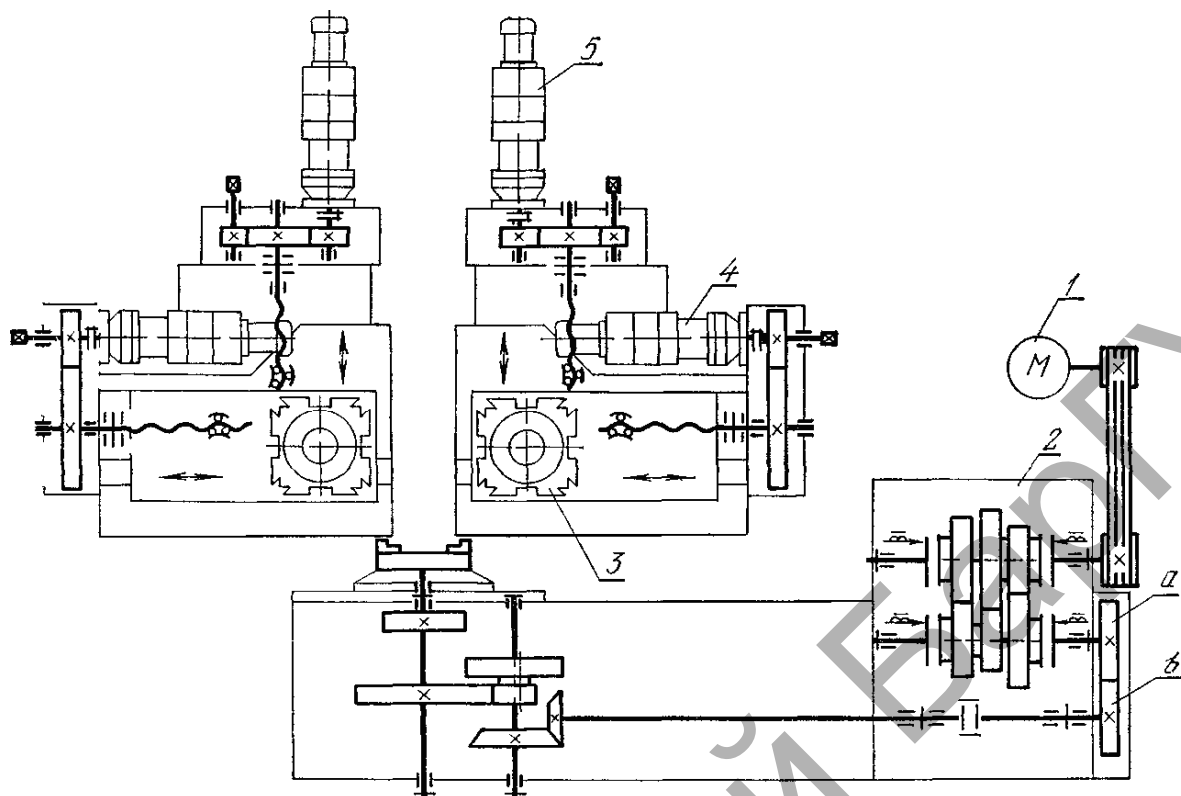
Кинематическая схема токарного полуавтомата с ЧПУ модели 1734Ф3
